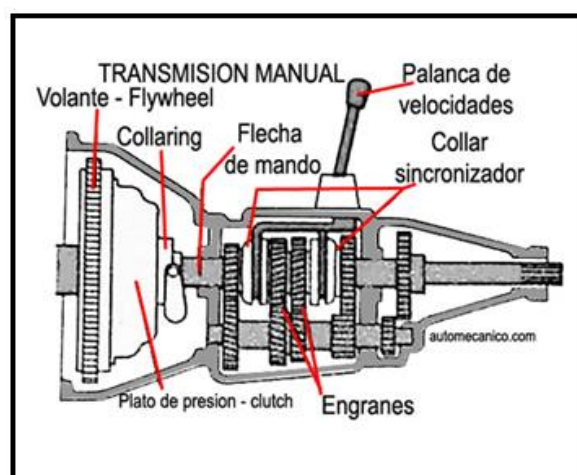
Partes de la transmisión manual. Fuente: automecanico.com [35]
